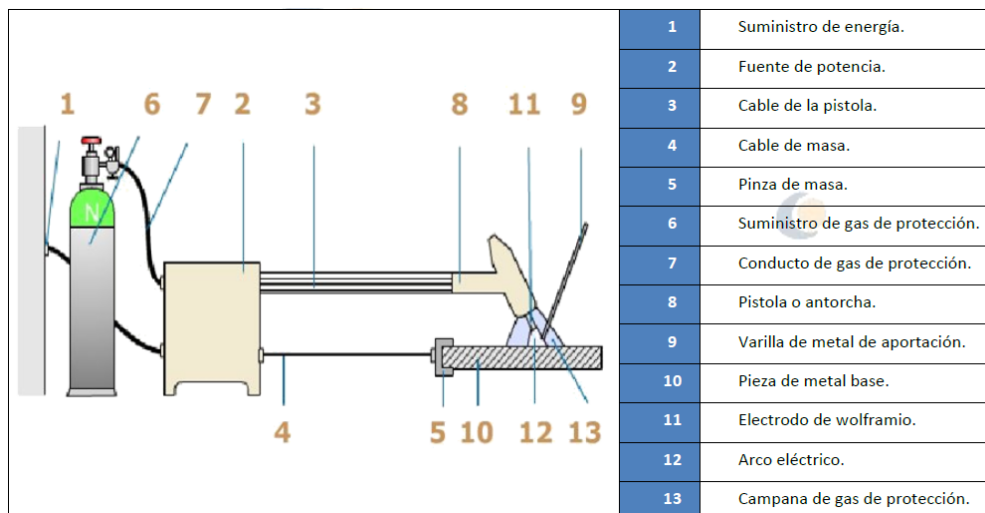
Instalación típica para soldadura TIG [7]
